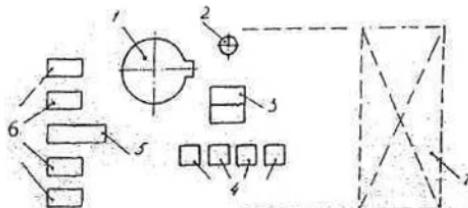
Примерная схема рабочего места литейщика: 1 – печь; 2 – ковш для расплавленного металла; 3 – контейнер с добавлениями; 4 – опоки под заливку; 5 – формовочная машина; 6 – опоки под формовку; 7 – подъемно-транспортное устройство
